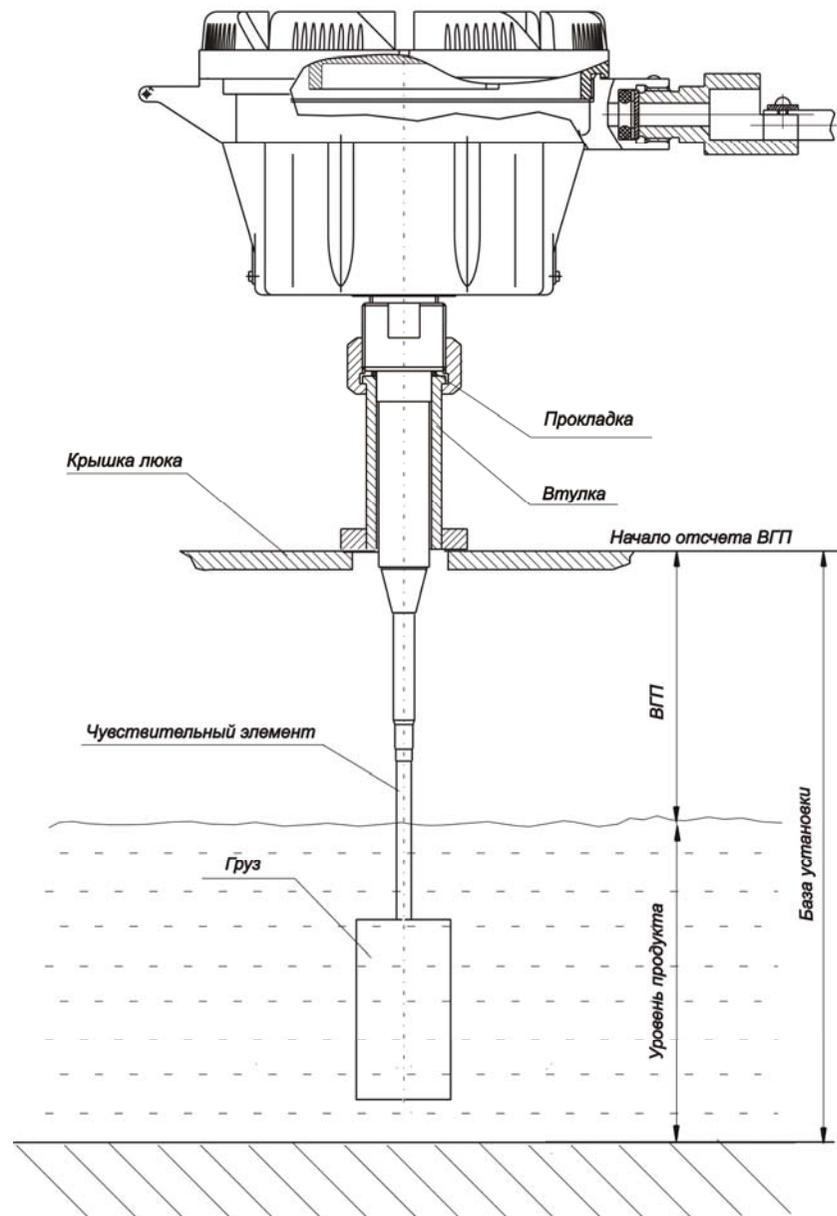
Внешний вид датчика УТР1 на резервуаре
